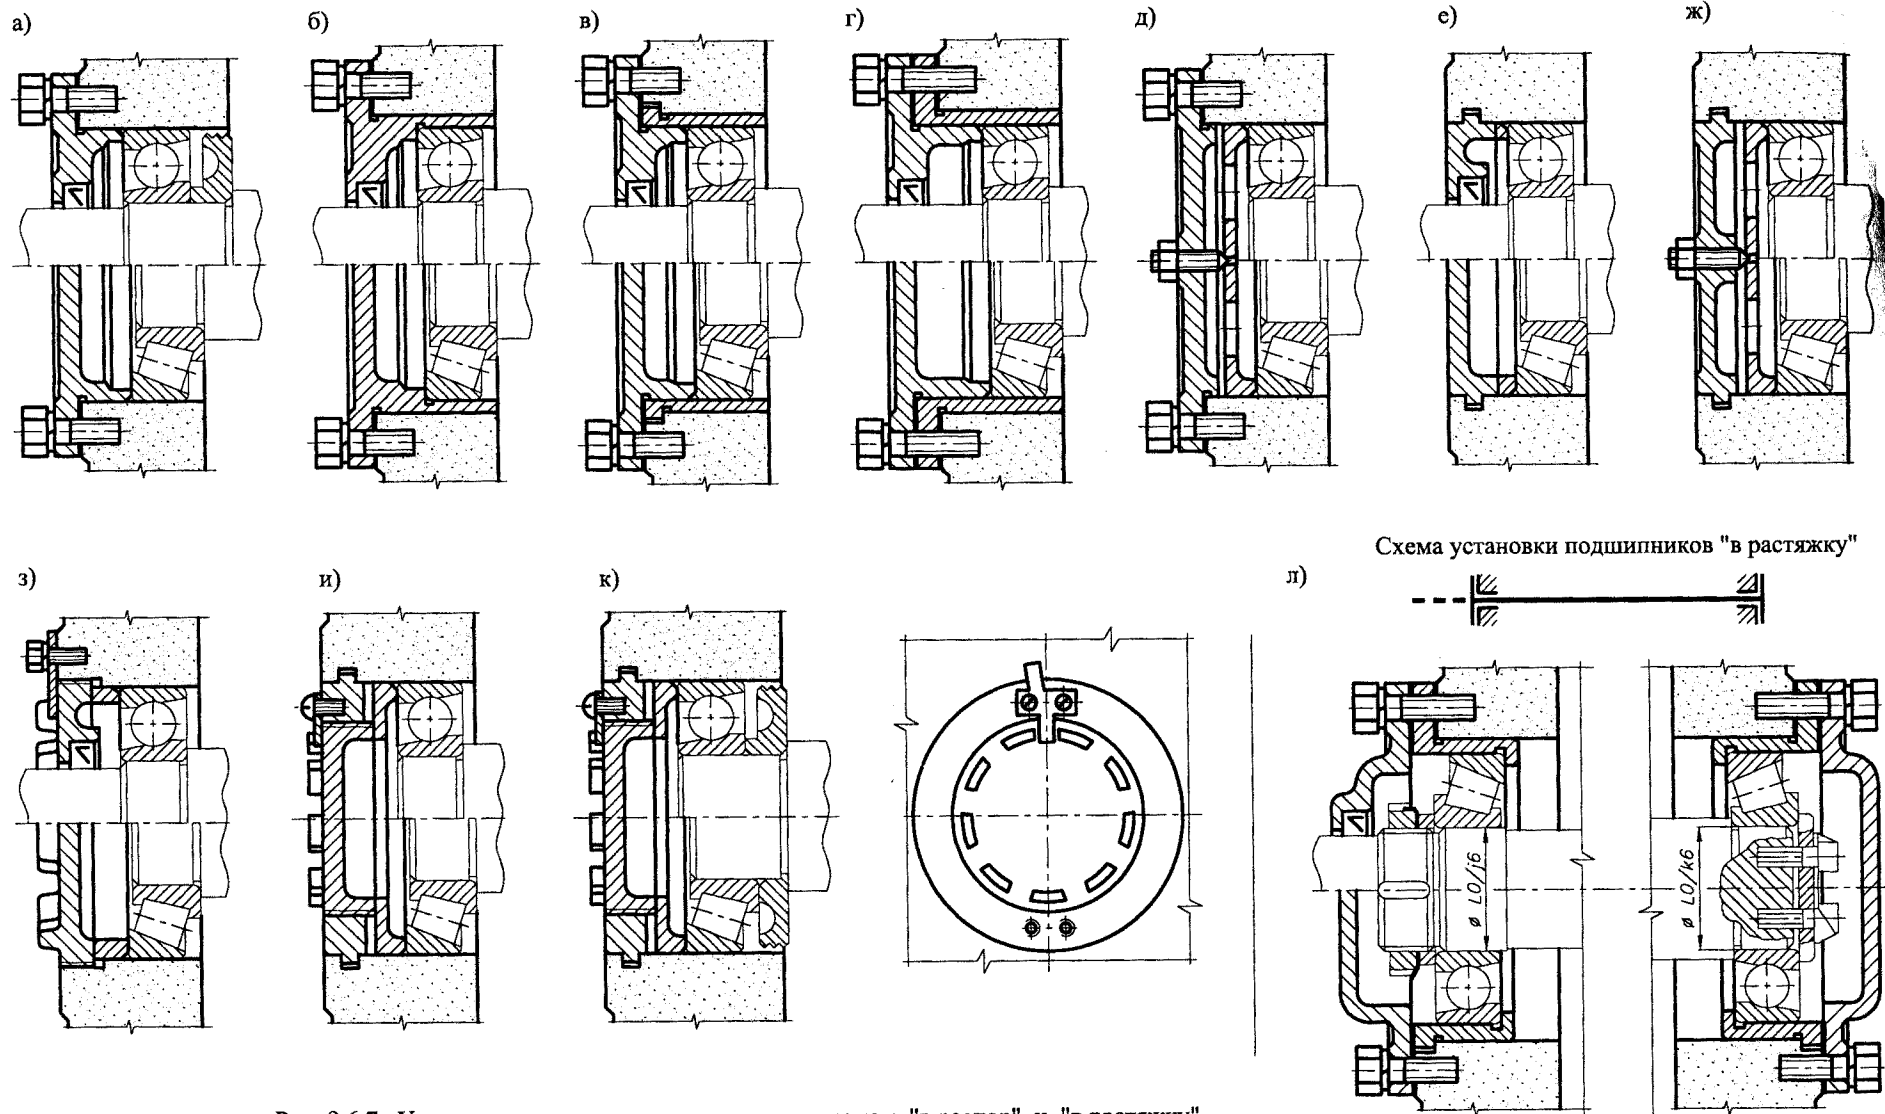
Установка в корпусе подшипников по схемам "в распор" и "в растяжку"
